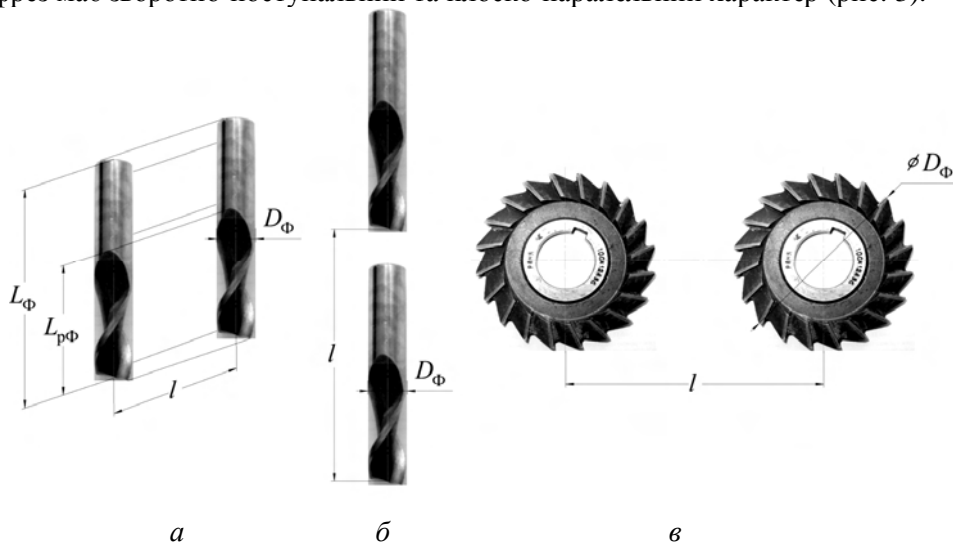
Загальний вигляд панданних зон фрезерного інструмента: а, б – пальцевої фрези; в – дискової фрези
